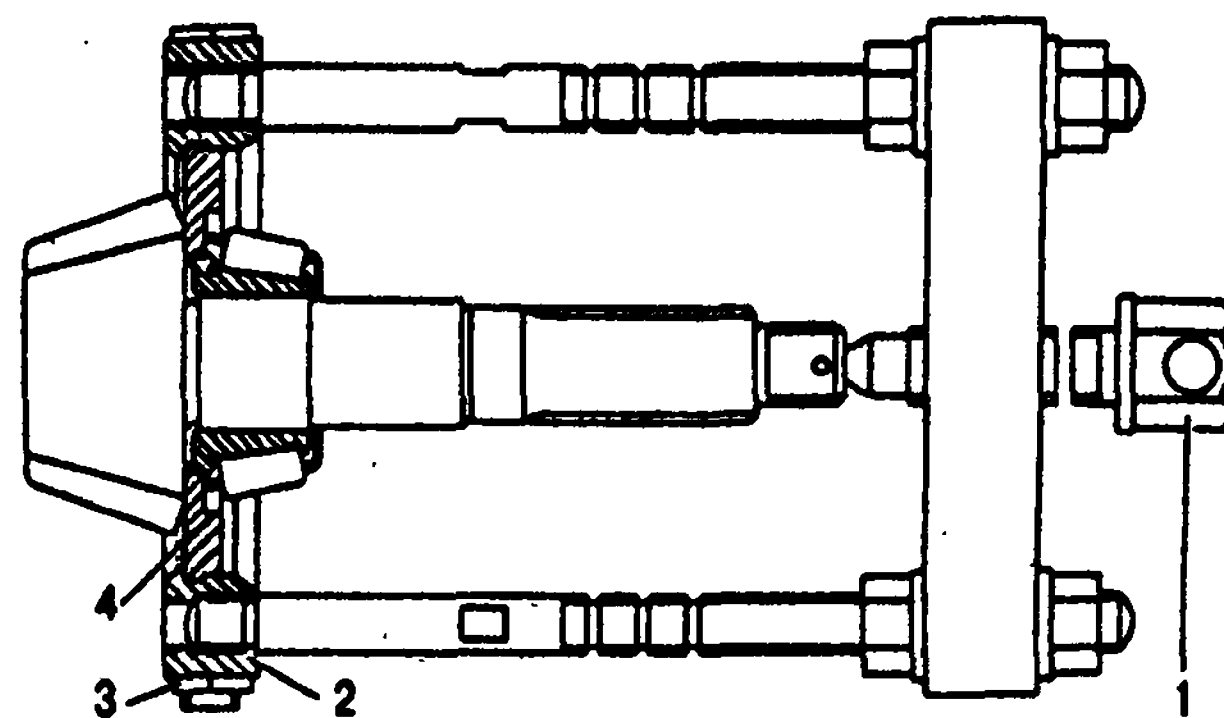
Снятие внутреннего кольца заднего подшипника с ведущей шестерни: 1 - винт; 2 - опора; 3 - гайка; 4 - вкладыш
